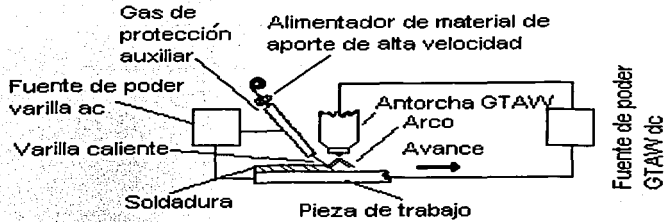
Esquema que muestra los componentes y parámetros del proceso de soldadura GTAW automatizado [6].
